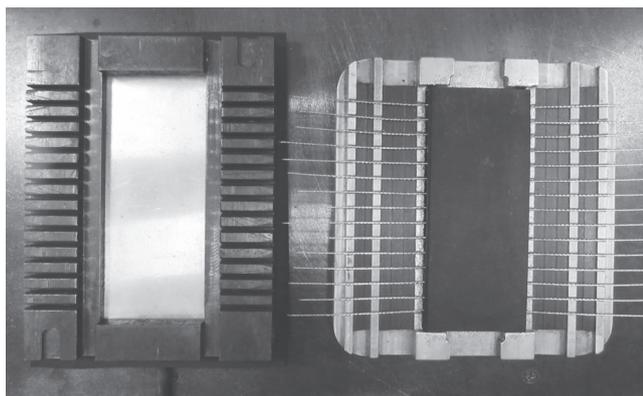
Пресс-форма для вулканизации, пресс-форма предварительной сборки и готовый резинокордный блок метода потребителя № 2
